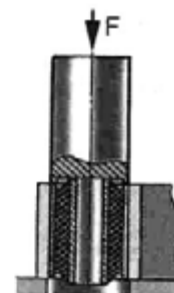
Выпрессовка шарнира из ушка рессоры
